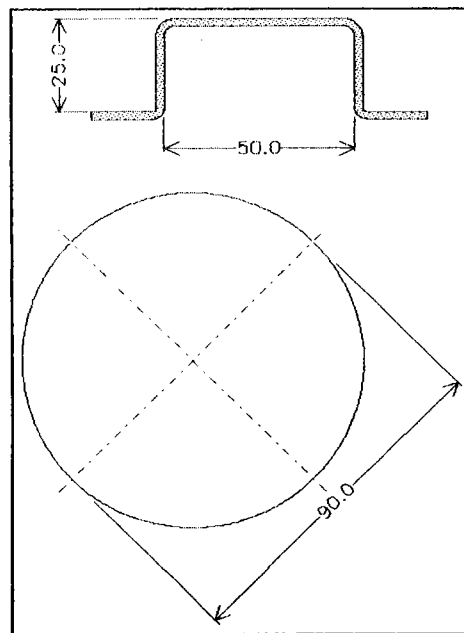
Dimensions du flan pour l'essai de cup-test.
